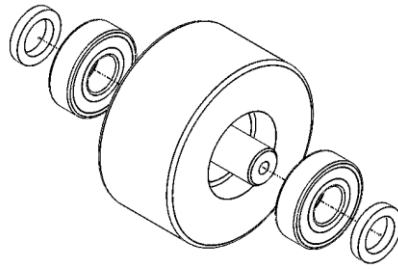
Perspetiva isométrica explodida "Assembly roletes preguiça".
